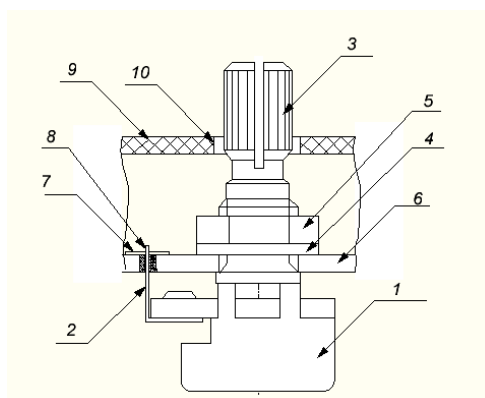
Фрагмент изделия в месте установки резистора типа WH186-1A-5 или ему аналогичных по конструкции выводов: 1 – корпус резистора; 2 – формовка выводов с установкой в отверстия в печатной плате; 3 – ось переменного резистора под ручку; 4 – шайба; 5 – гайка; 6 – плата; 7 – контактная площадка; 8 – паяное соединение; 9 – лицевая панель крышки; 10 – отверстие в крышке для прохода оси резистора при сборке изделия
